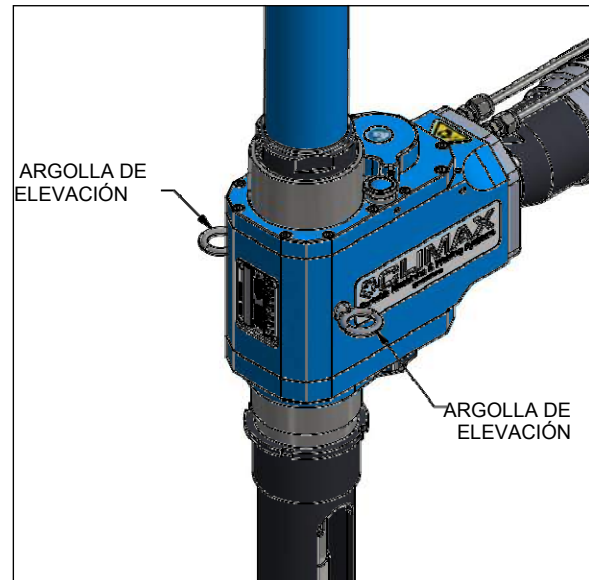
UBICACIÓN DE LAS ARGOLLAS DE ELEVACIÓN
